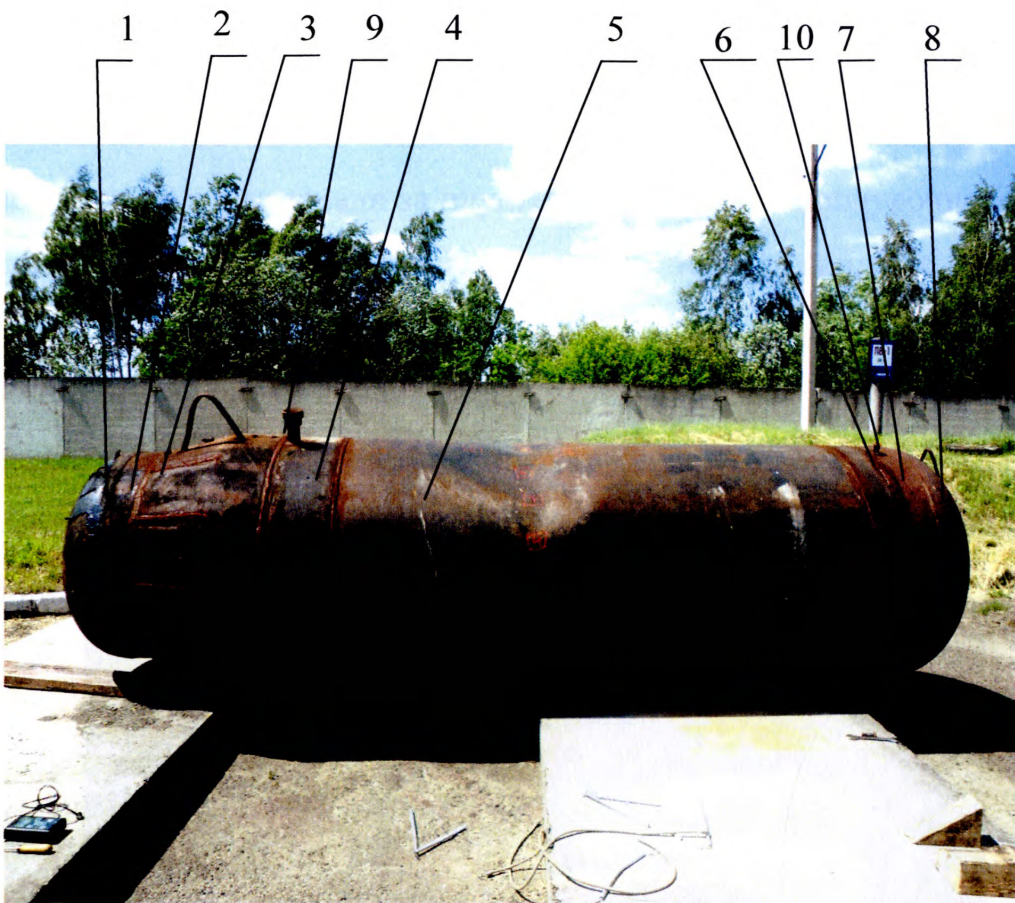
Загальний вигляд випробувального напірного резервуара
